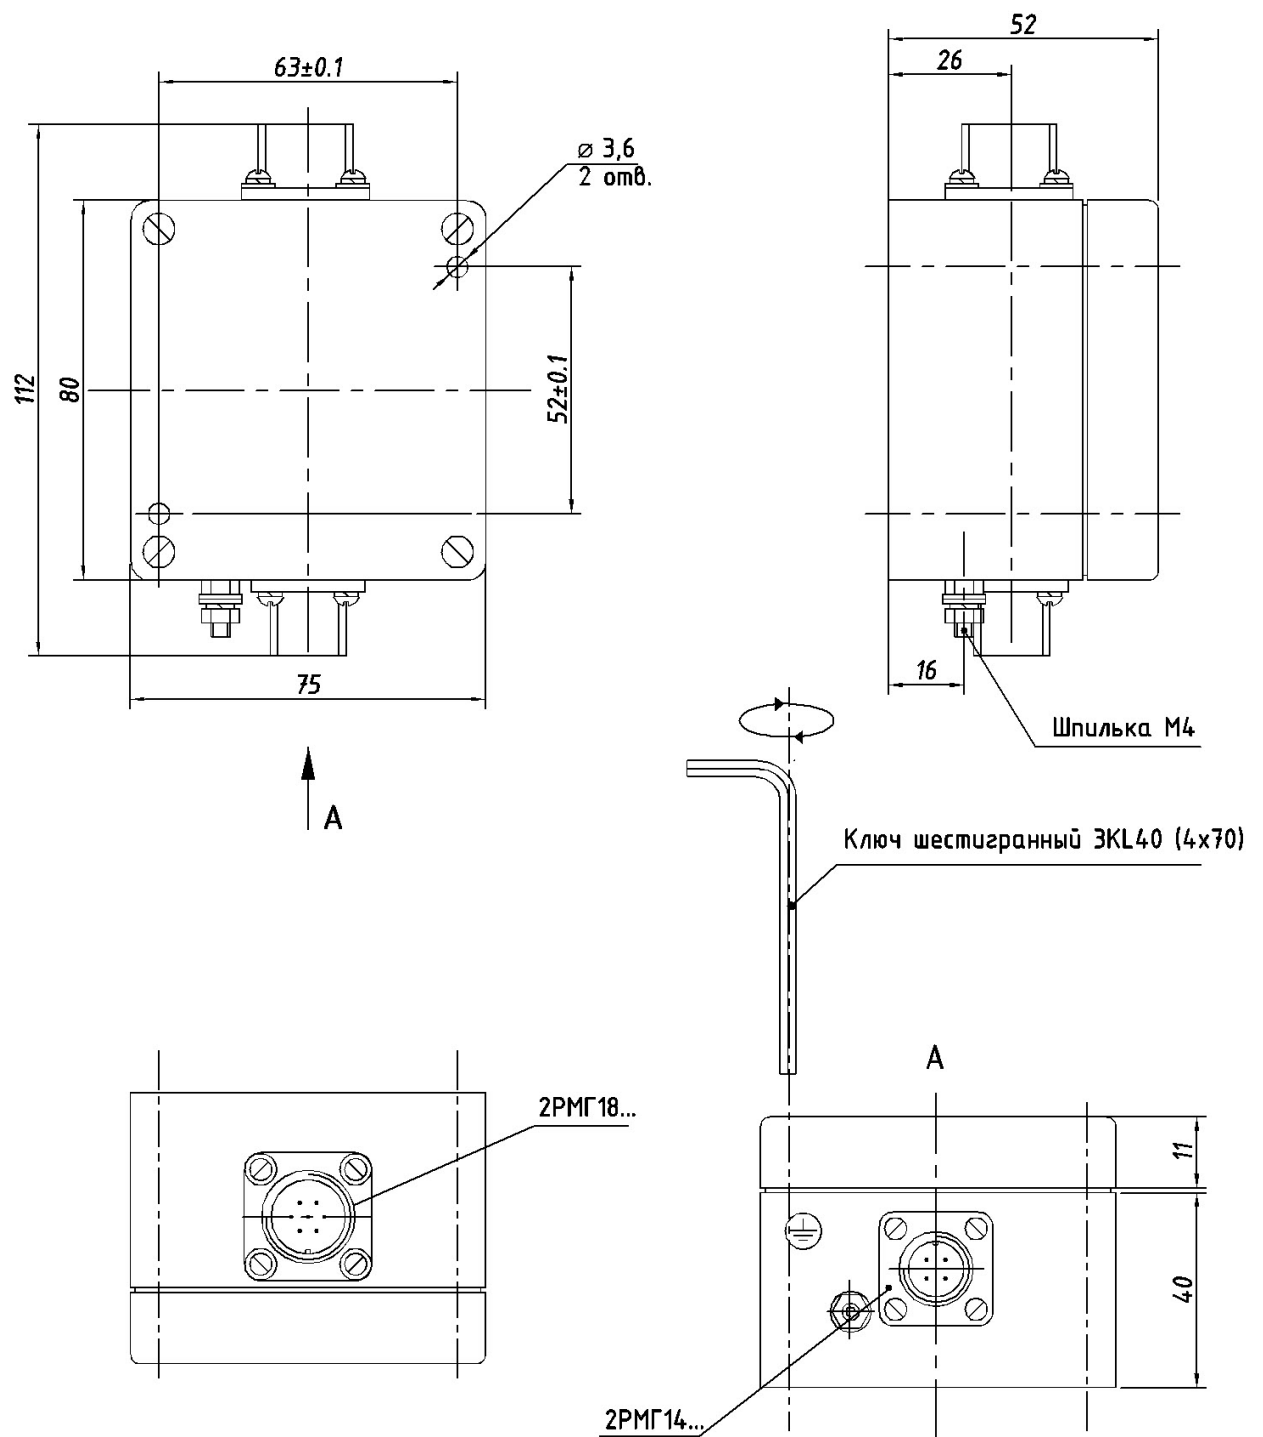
Габаритные и установочные размеры выносного усилителя сигнала
